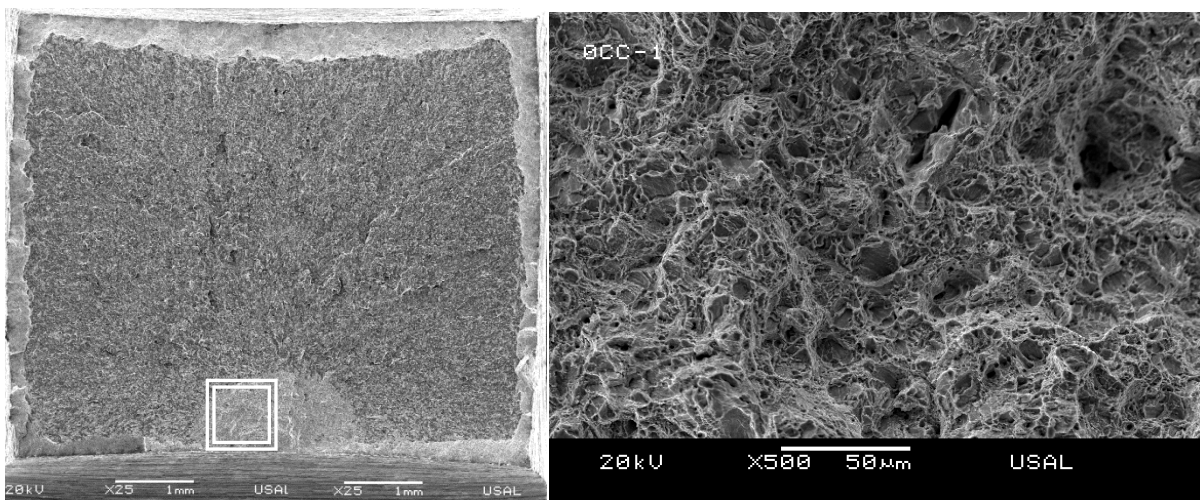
Micro-fractografía de la zona de proceso de fractura de la probeta B0-CC-1.
